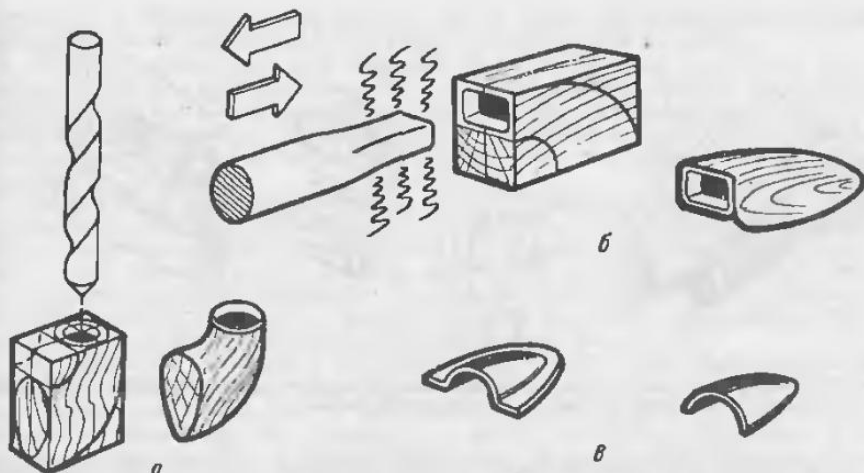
Изготовление воздухозаборников: а - сверлением; б - выжиганием; в - штамповкой
